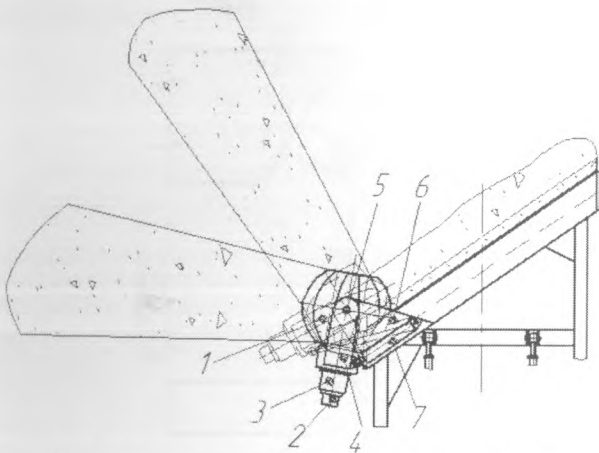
Косовстановлений відвальний робочий орган із лопатевим сферичним металником для керованого бічного транспортування ґрунту
